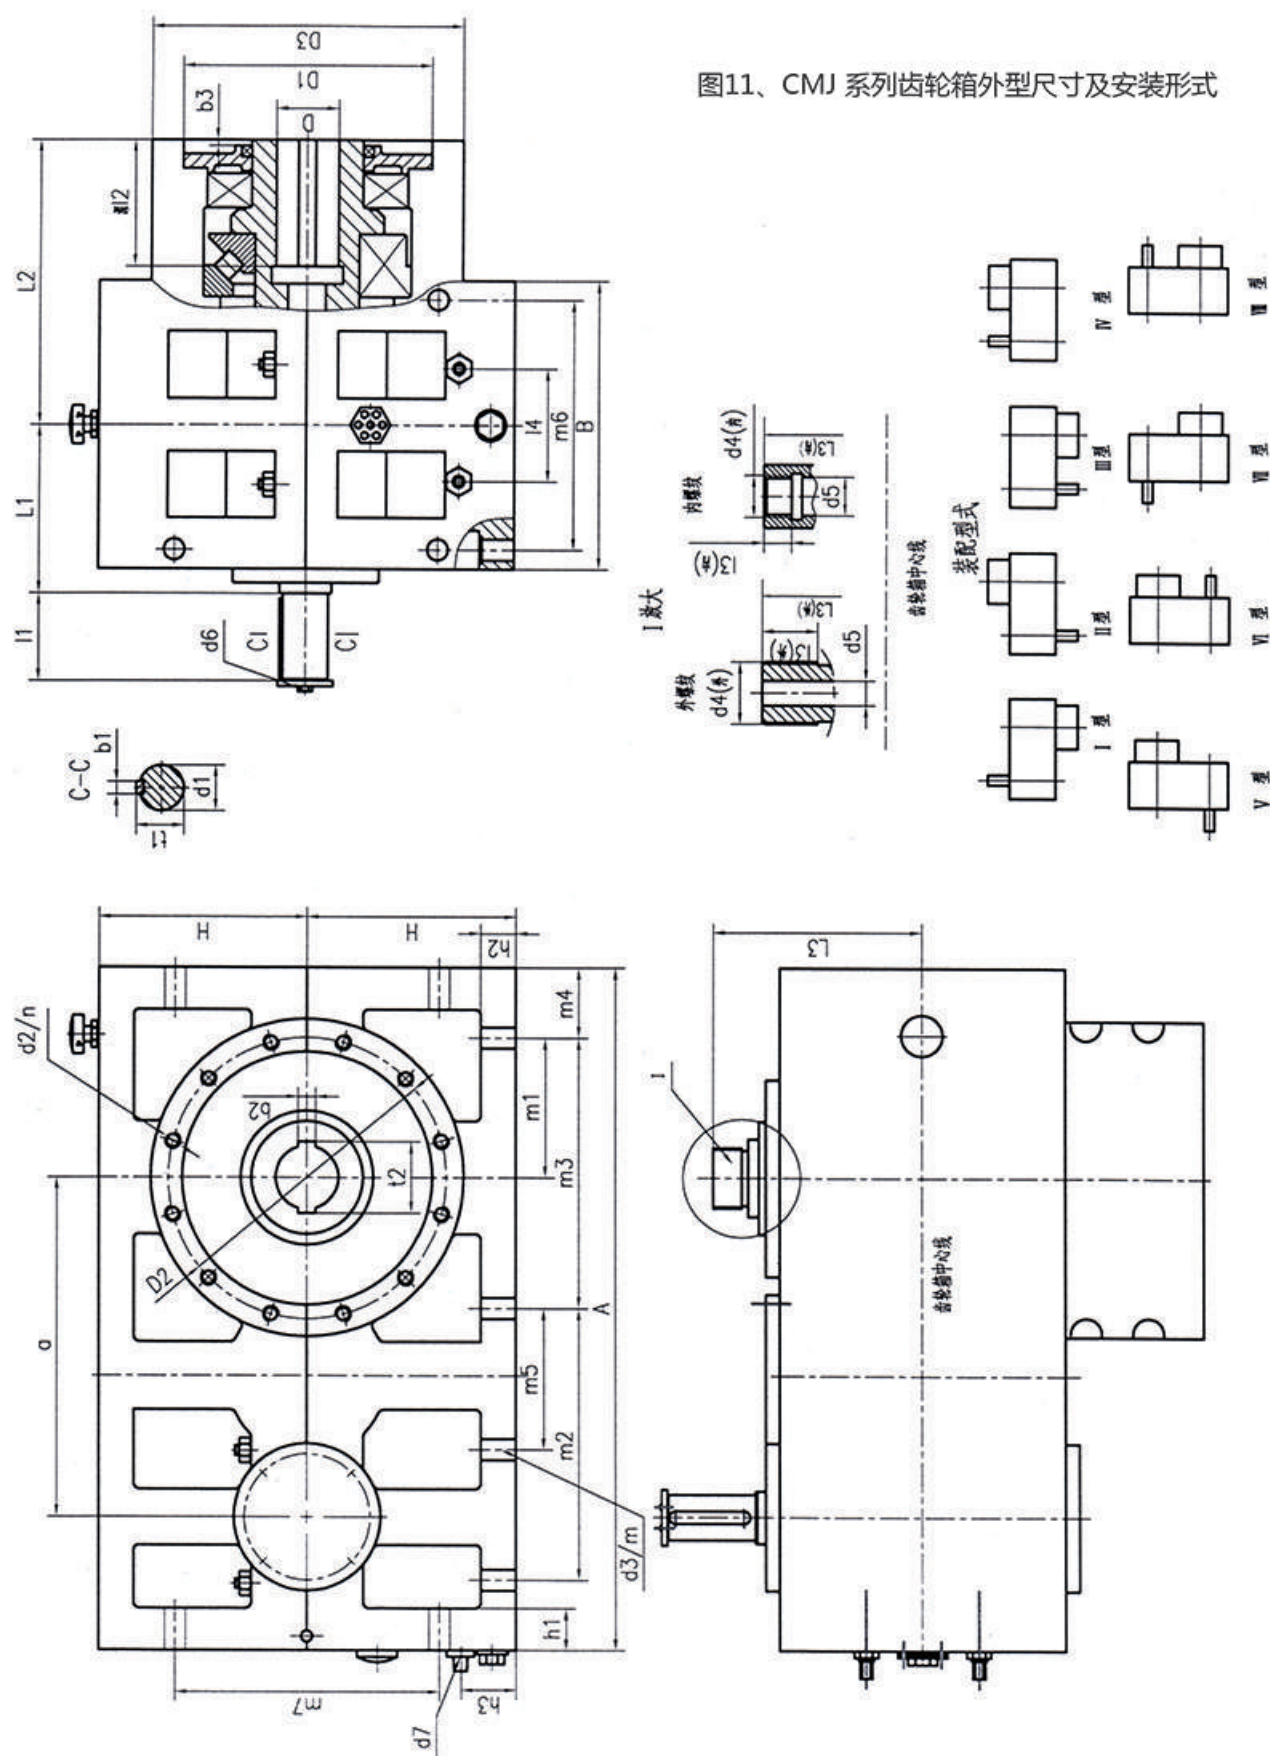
、CMJ 系列齿轮箱外型尺寸及安装形式
